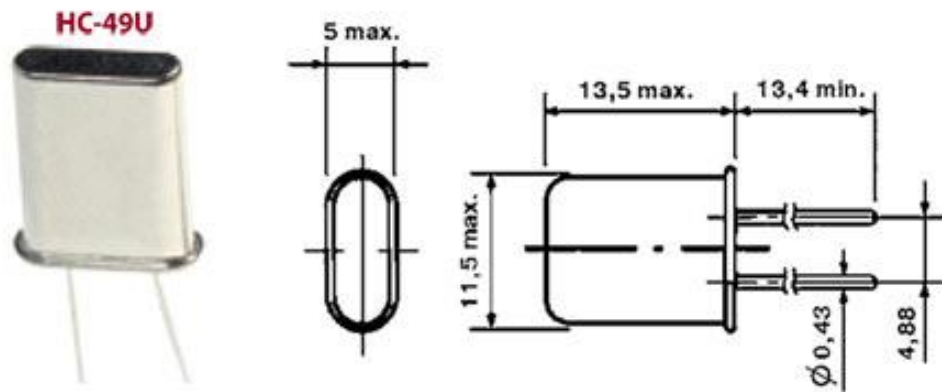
Габаритні розміри кварцевого резонатора HC-49U-4,032 МГц
